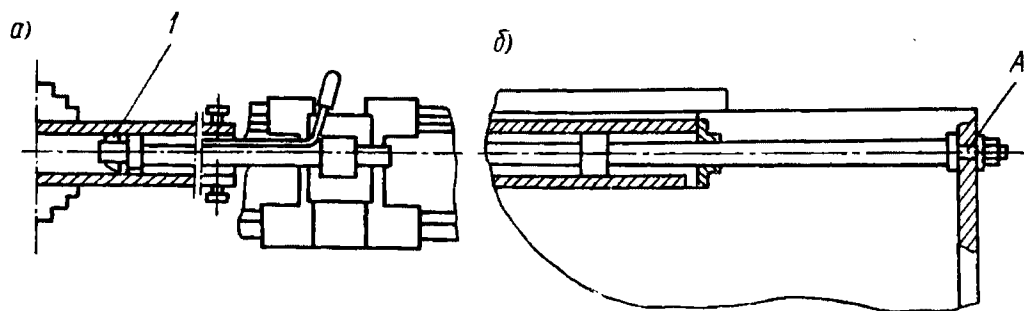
Гидроцилиндр: а — расточка отверстия цилиндра; б — расточка отверстия на станине
